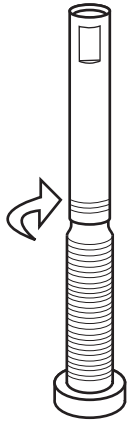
Vissez le prolongateur de valve en ligne sur la tige de valve.
